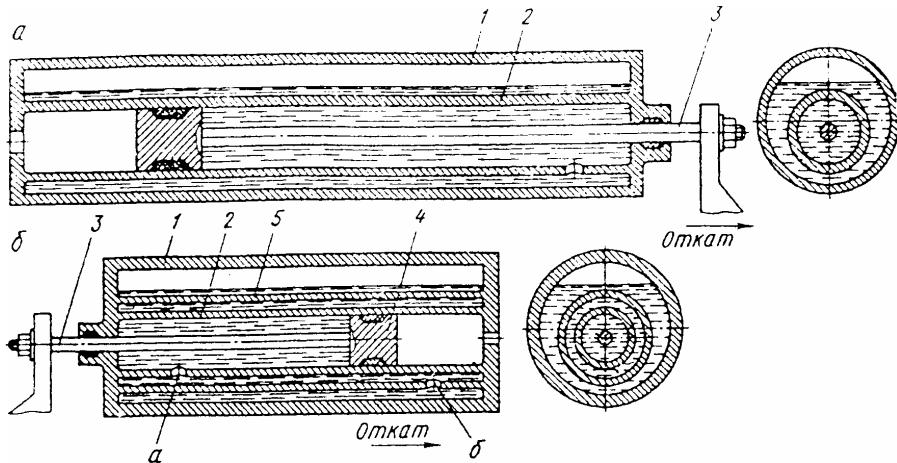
Гидропневматические накатники с охватывающими цилиндрами:
